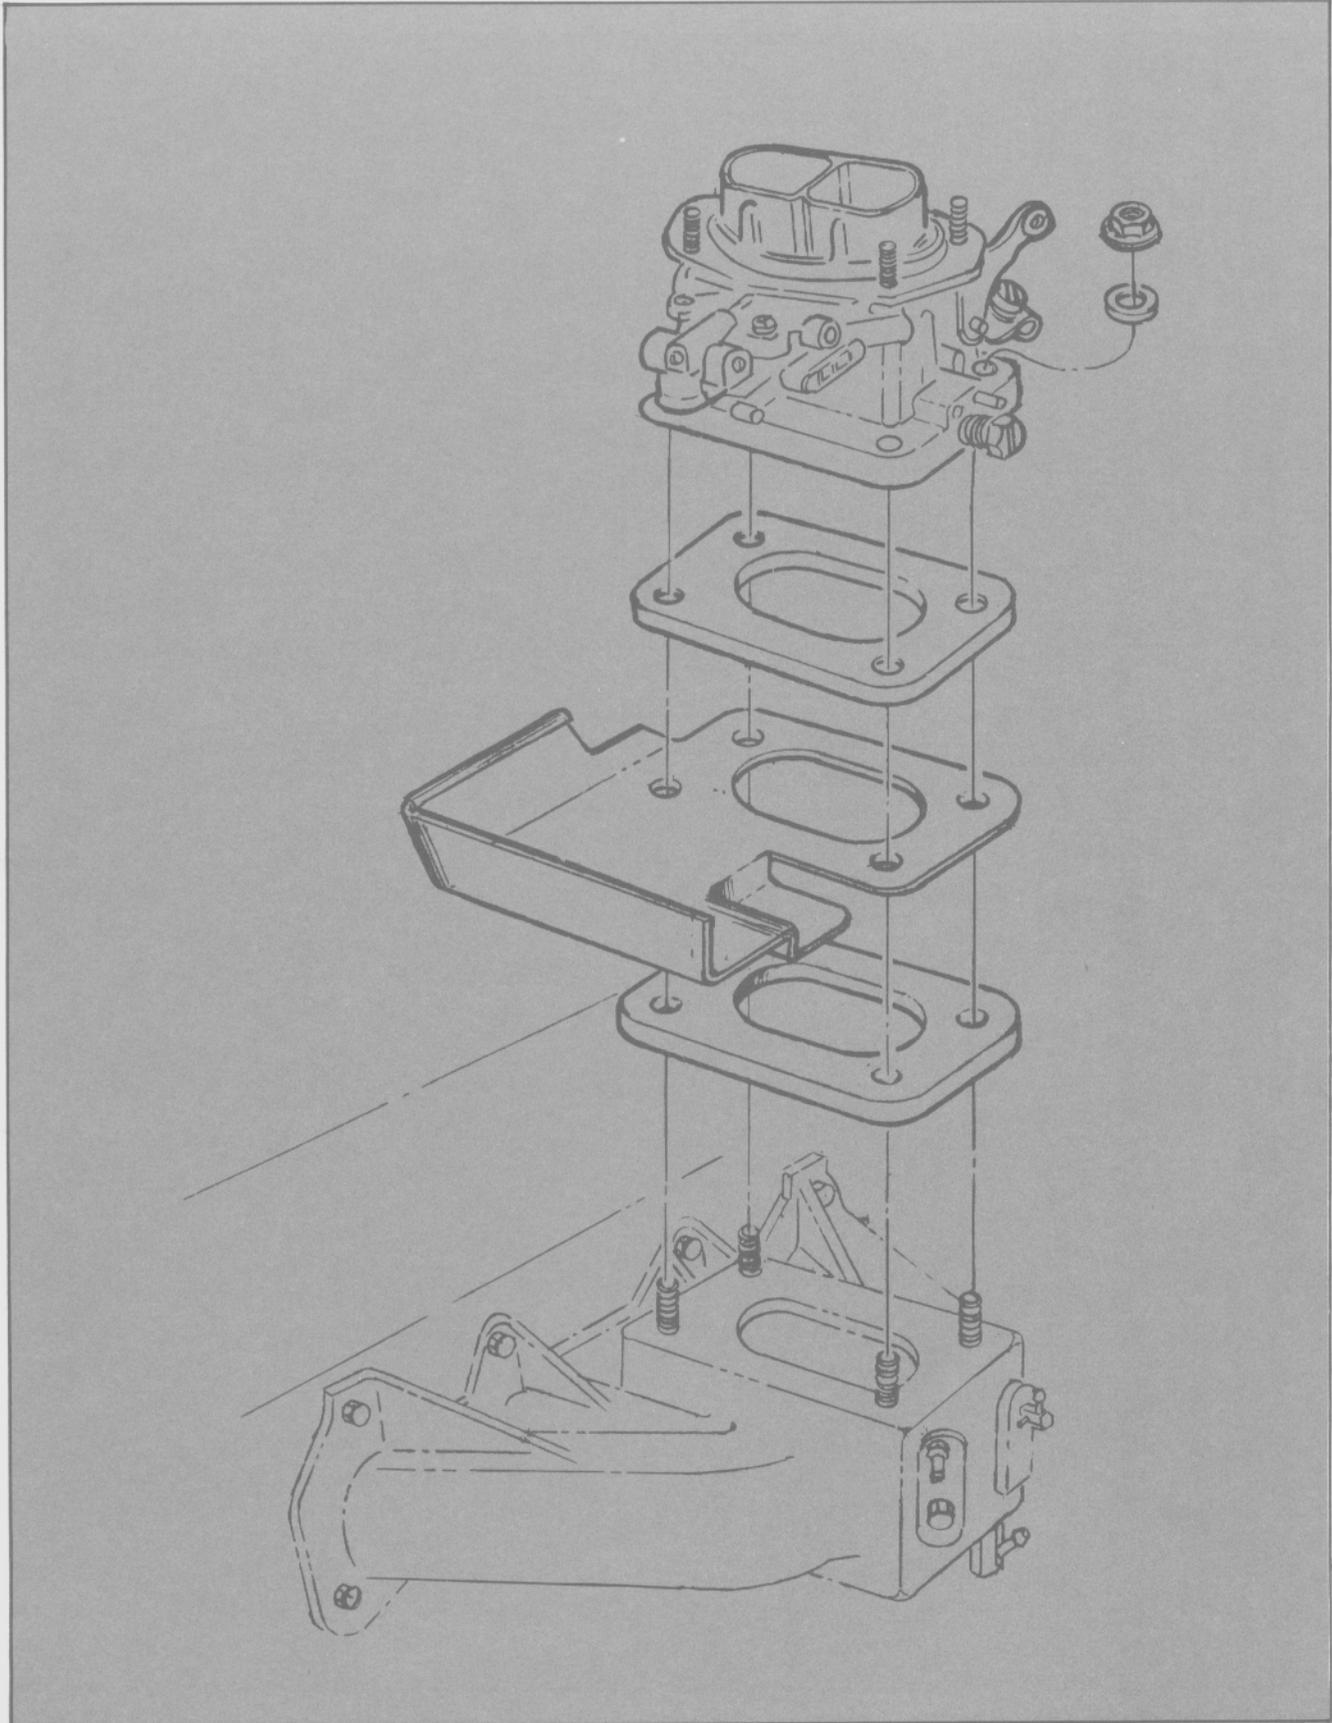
Detalle de instalación del carburador. Motor I4-2,3L.
